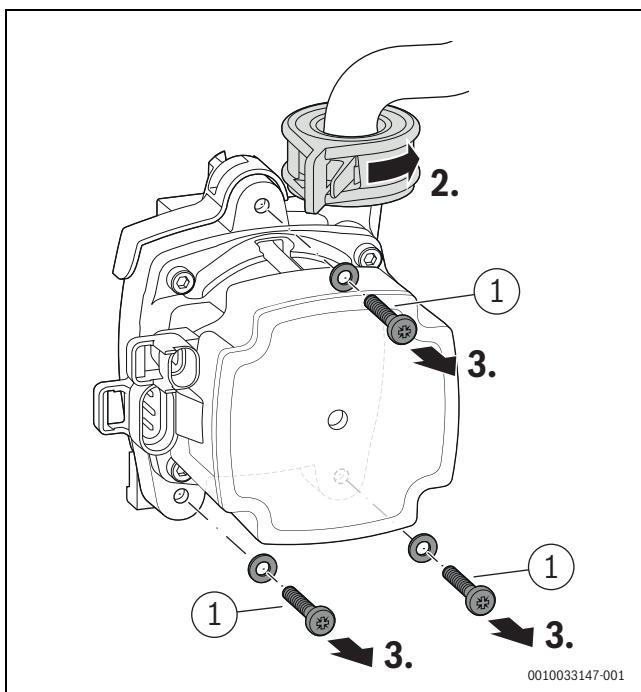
Déverrouiller la pompe de chaudière et retirer les vis
